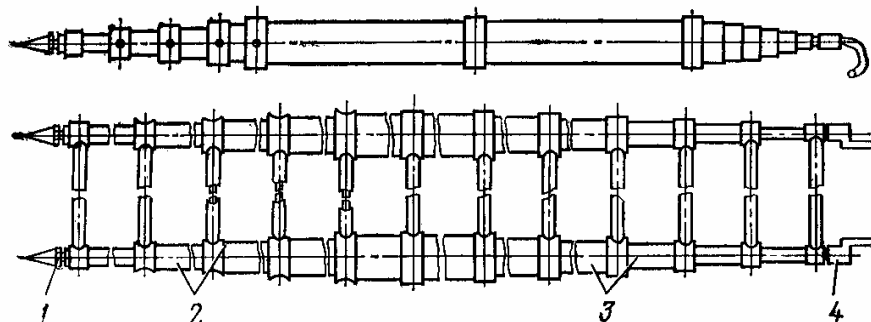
Бортовая раздвижная лестница 154.00.9901.000:
